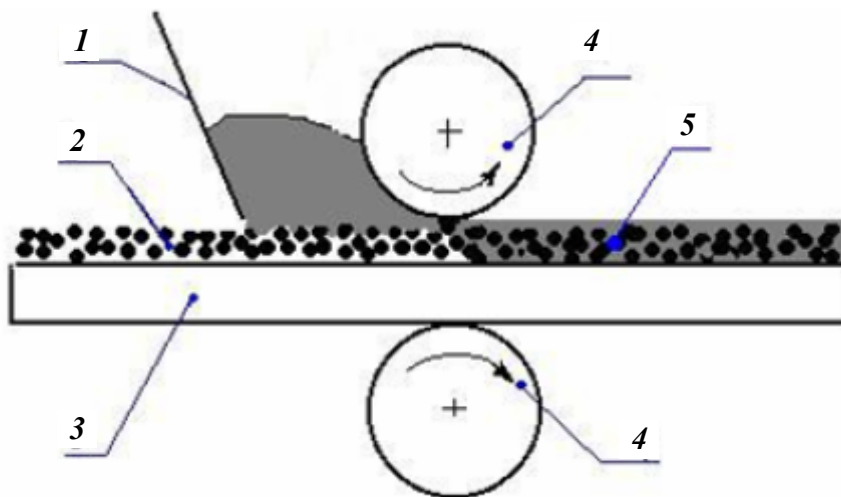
Схема пропитки бронзового слоя пастой фторопласта: 1 – бункер с пастой; 2 – пористый бронзовый слой; 3 – стальная основа; 4 – прокатные валки; 5 – пористый слой, пропитанный фторопластом
